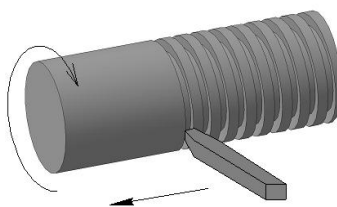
Схема нарезания резьбы на цилиндрическом стержне резцом
